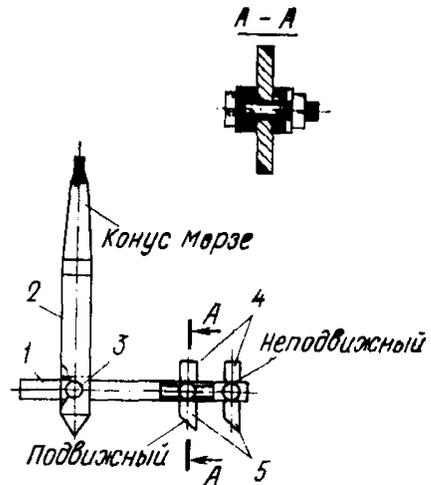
Приспособление для вырезки прокладок на сверлильном станке
